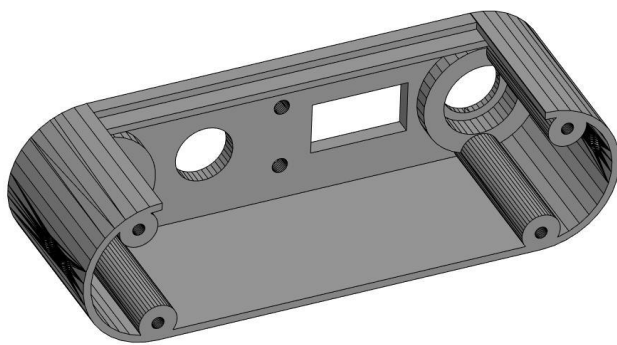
3D-модель корпусу прототипу робота-розвідника
